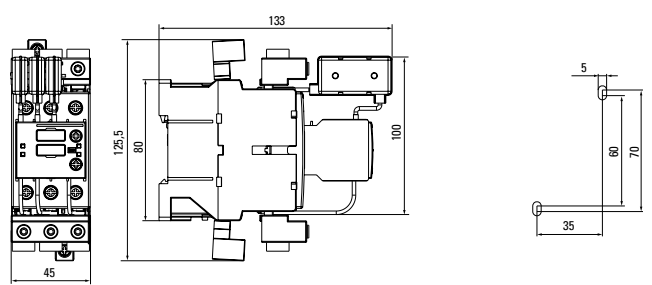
Габаритные и установочные размеры контакторов КМЭК 25, 30
